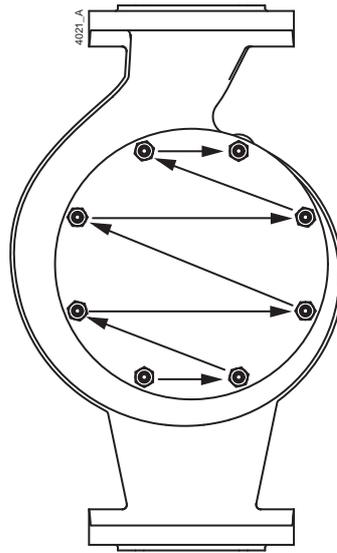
Séquence de desserrage des écrous de fixations de la pièce-lanterne.
